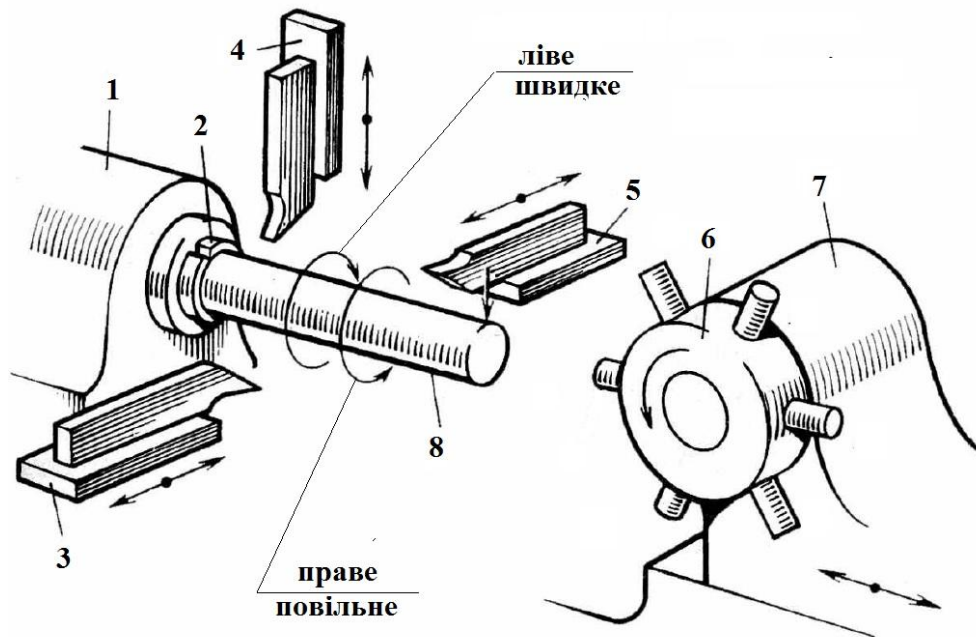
Схема роботи токарно-револьверного автомату, де: 1 – шпиндельний вузол, 2 – шпиндель із затискним цанговим патроном, 3 – передній поперечний супорт, 4 – верхній поперечний супорт, 5 – задній поперечний супорт, 6 – шестипозиційна револьверна головка, 7 – позовжній револьверний супорт, 8 – пруток
